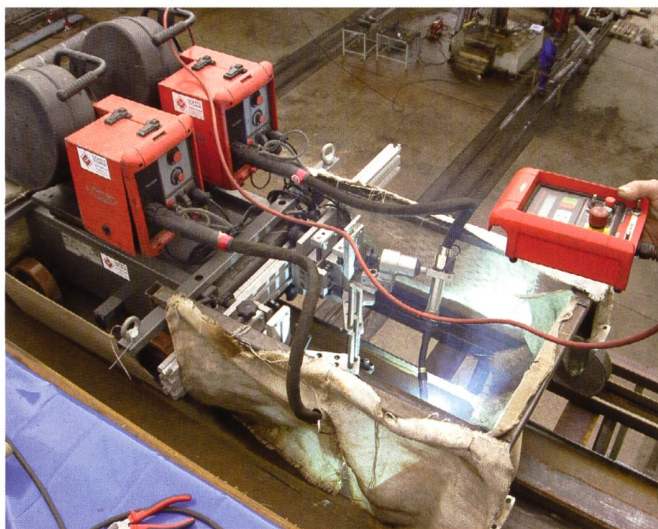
Anschweißen der Kranbahnschienen mittels Roboter.
